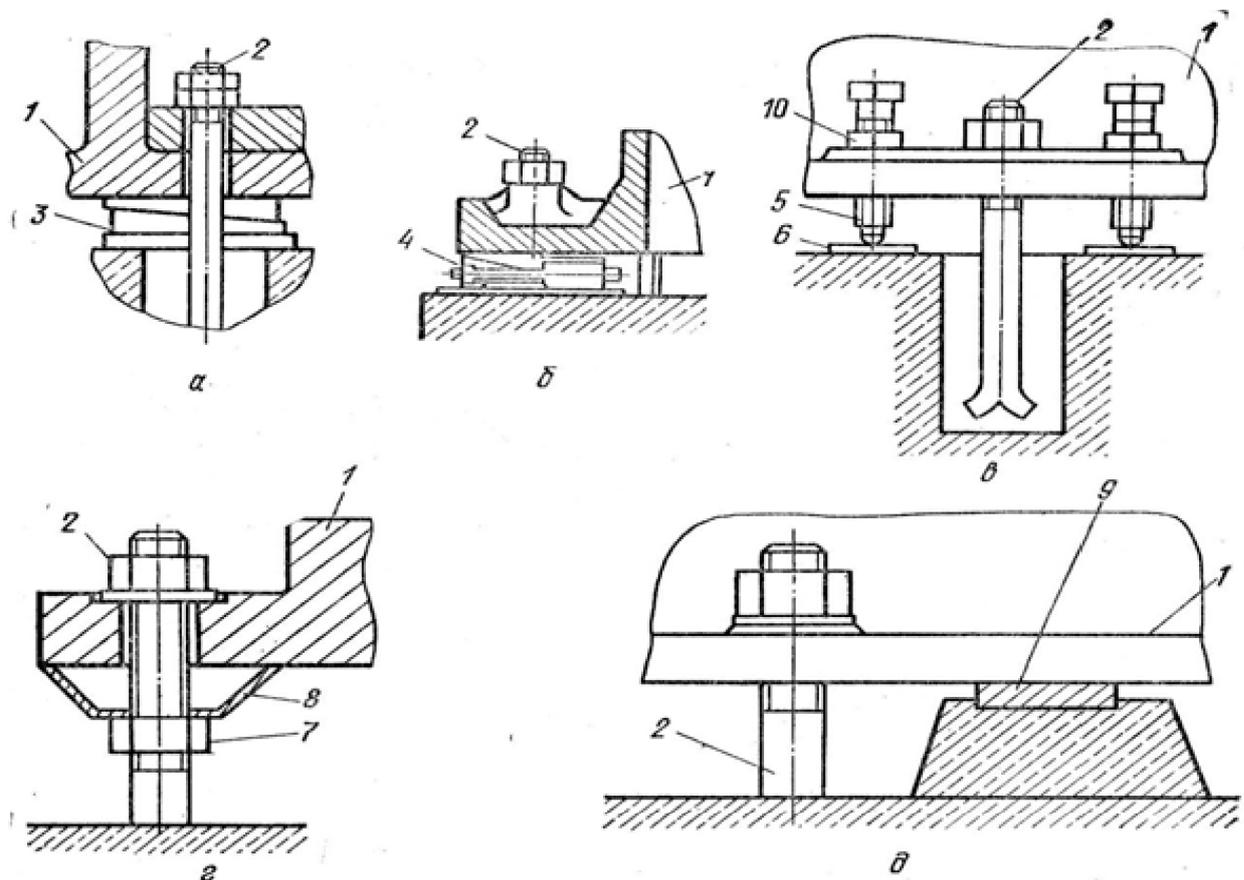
Установка и выверка оборудования на подкладках и бесподкладочным методом:
